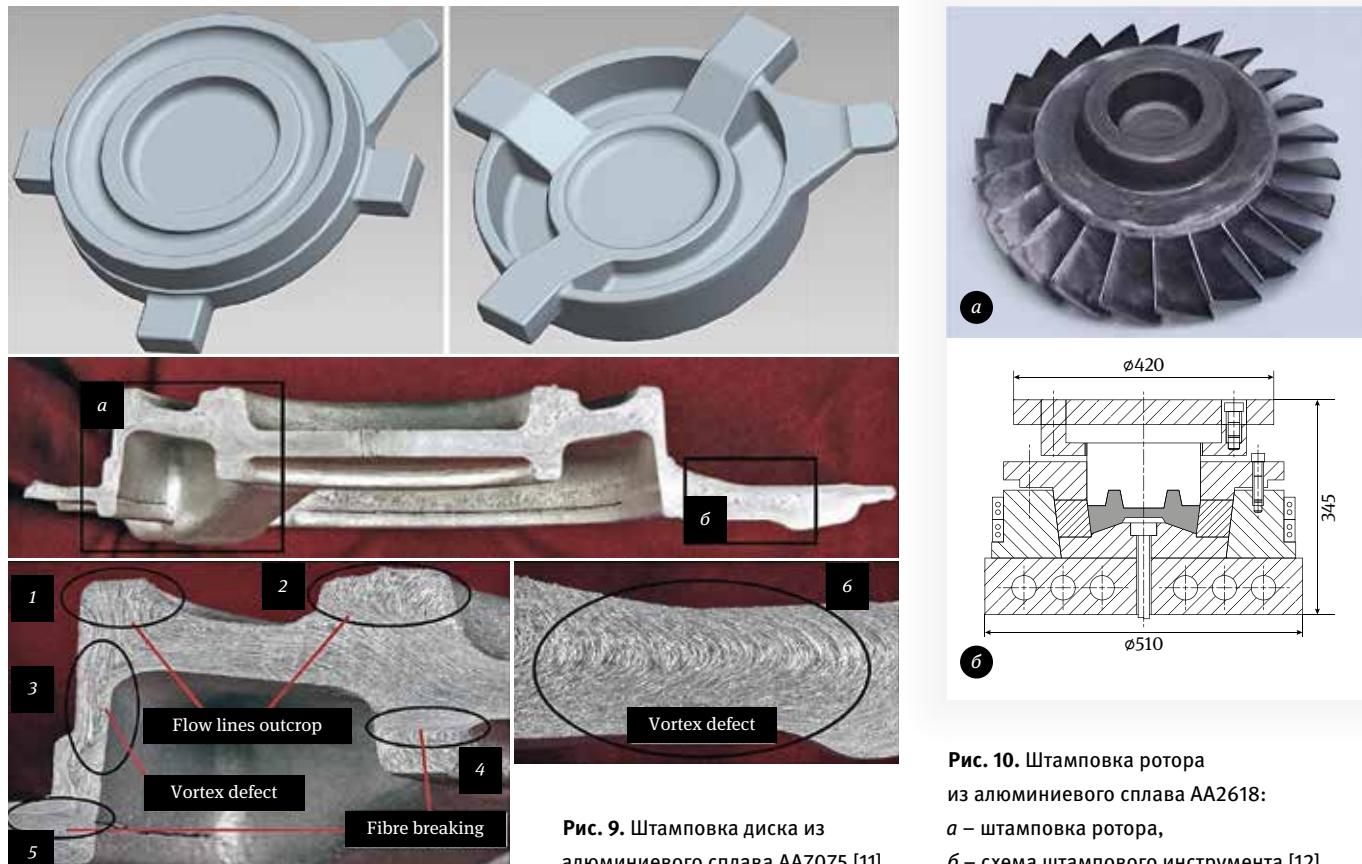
Штамповка ротора из алюминиевого сплава AA2618:
